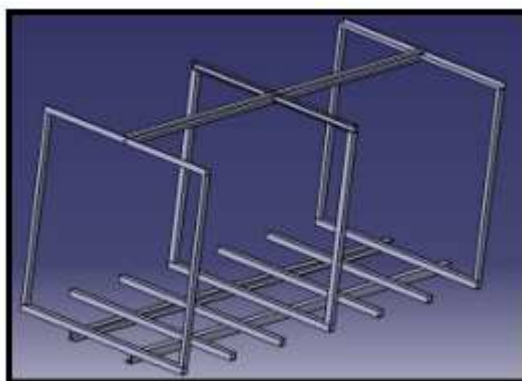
7: Estructura fija. Detalle viga longitudinal
